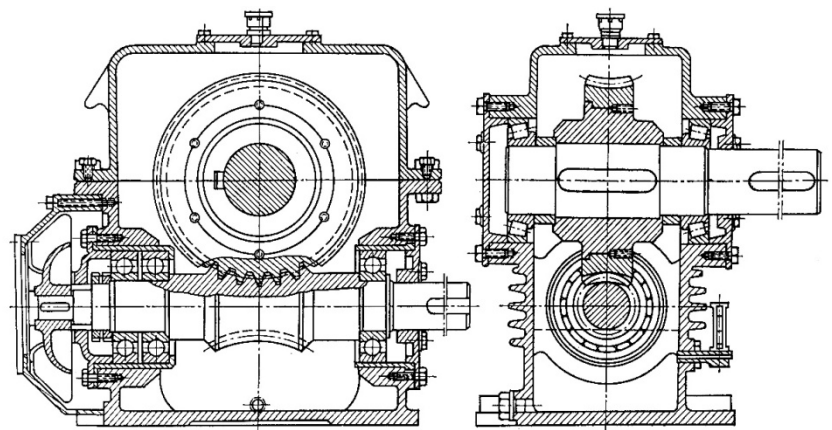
Reductor de tornillo sin fin-corona. Ejes montados sobre rodamientos en disposición fijo-libre (Ref.1)
